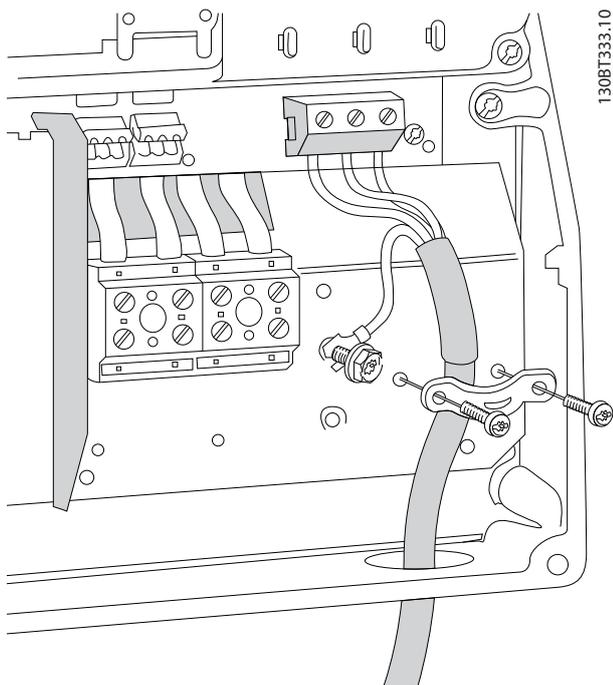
Подключение двигателя, корпуса В1 и В2
